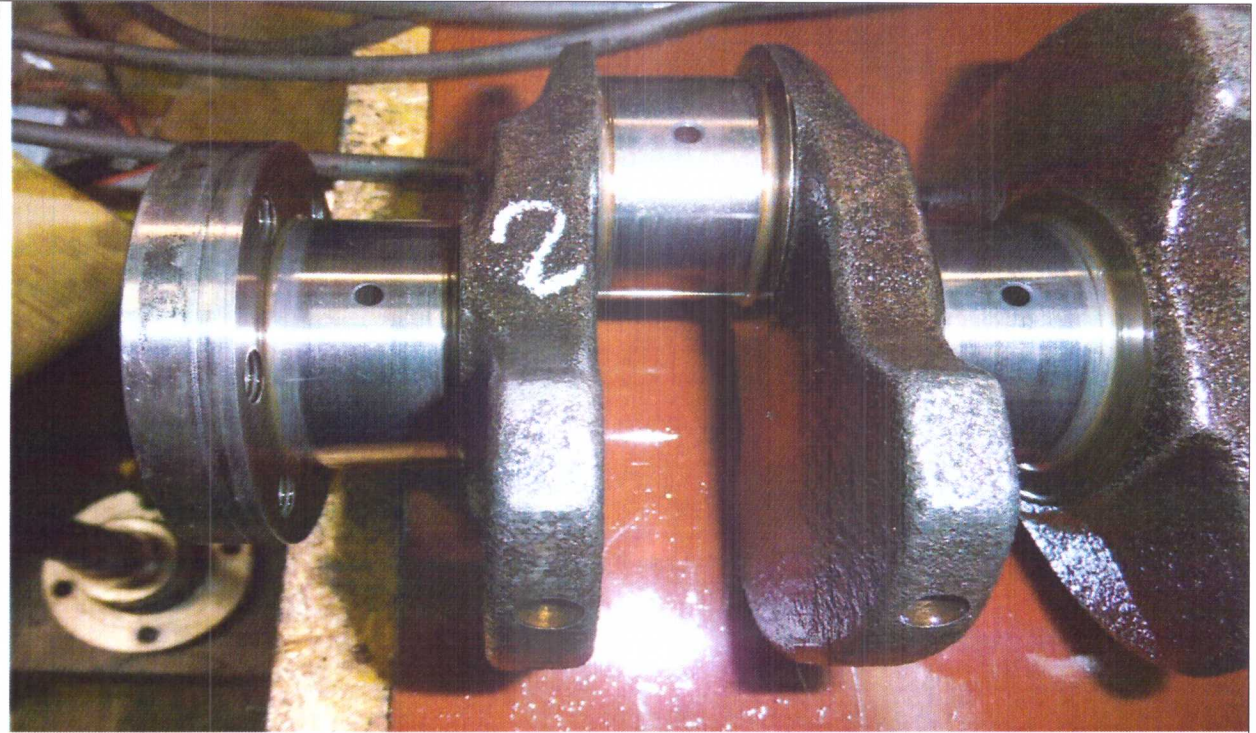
Внешний вид шеек коленчатого вала по окончании длительных испытаний двигателя при работе на базовом масле Castrol EDGE
